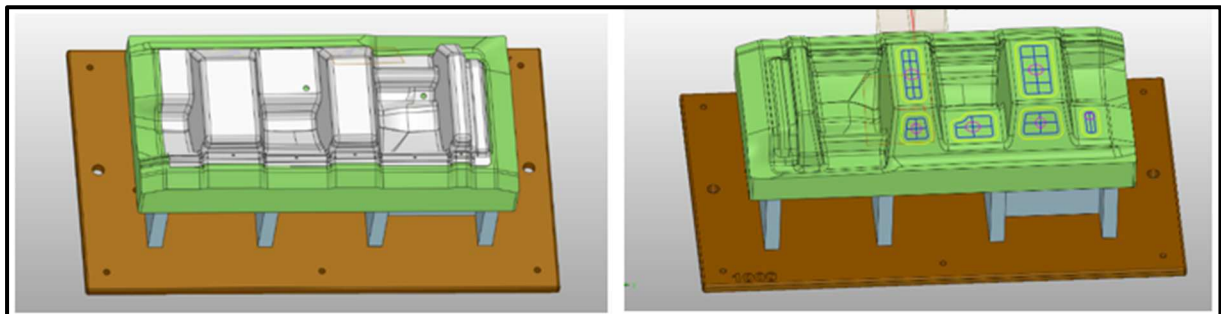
Fräsaufnahme zu Testwerkzeug / 28.02.24 Lakowa intern.
